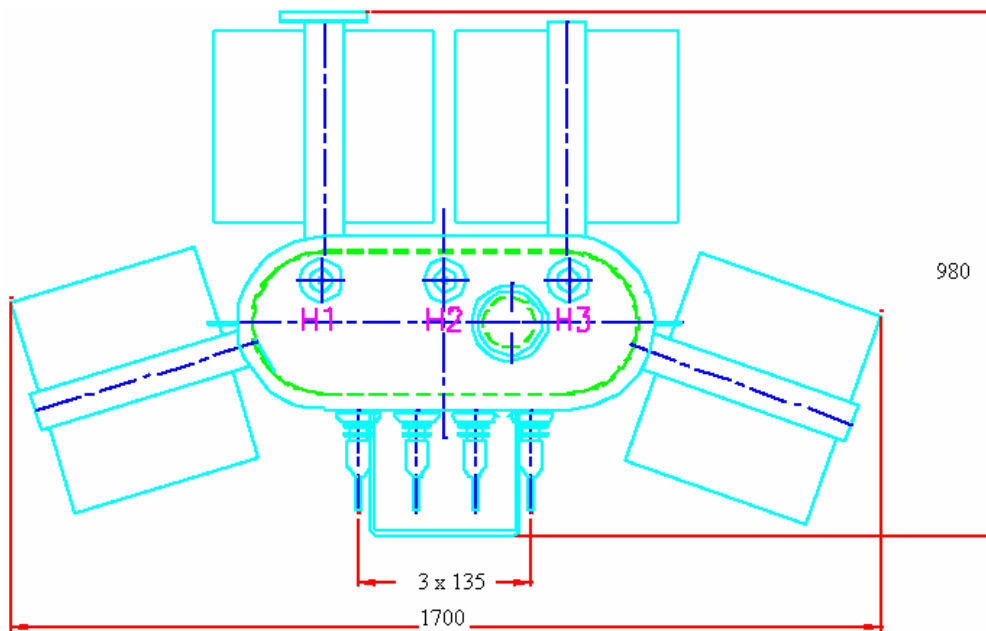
Vista em Planta do Transformador de 300 kVA
